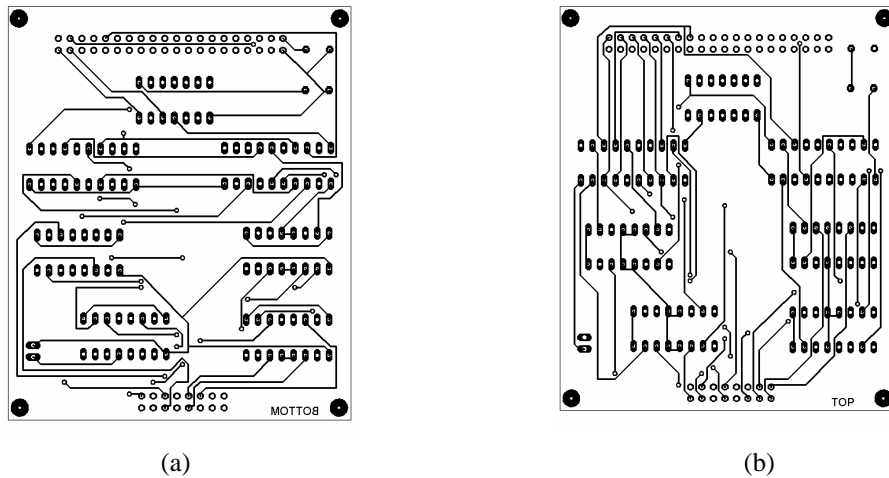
Circuito impreso de la tarjeta de control cuarta parte. (a) Diseño inferior (b) Diseño superior.
